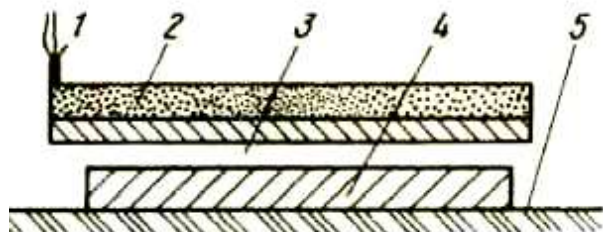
Схема зварювання вибухом двох металевих пластин: 1 – детонатор; 2 – заряд ВР; 3 – метана пластина; 4 – нерухома пластина; 5 - основа
